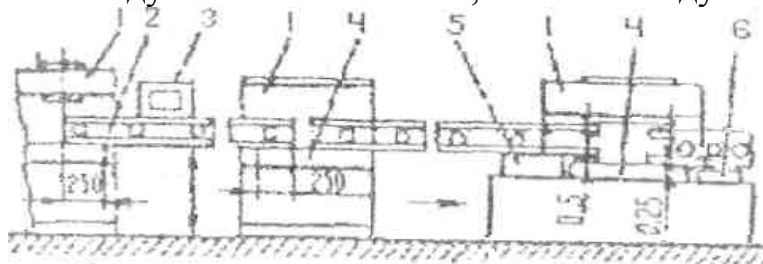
Взаимное расположение станков АЛ: 1 – станки АЛ; 2 – контрольная линейка; 3 – уровень; 4 – базовая планка приспособления станка; 5, 6 – промежуточные планки (направляющие)
